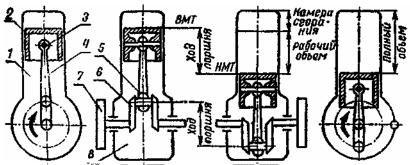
Схема двигателя внутреннего сгорания: 1 - цилиндр; 2 - поршень; 3 - поршневой палец; 4 - шатун; 5 - нижняя головка шатуна; 6 - коленчатый вал; 7 - маховик; 8 - картер
